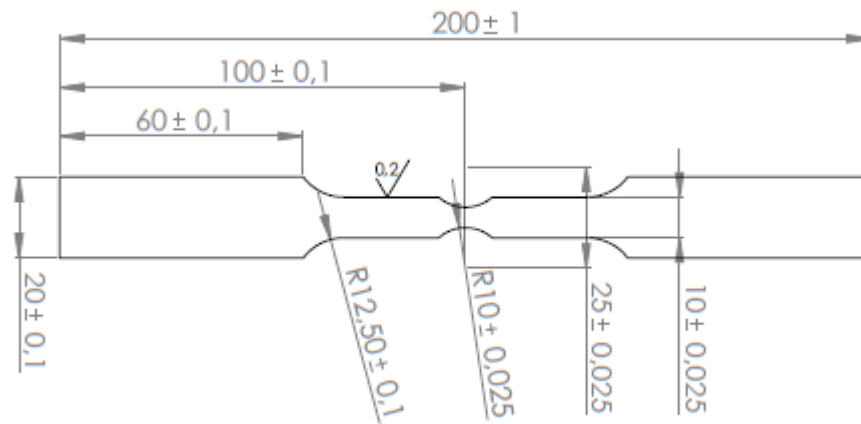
Dimensões do corpo de prova retangular com entalhe de 10 mm de raio
